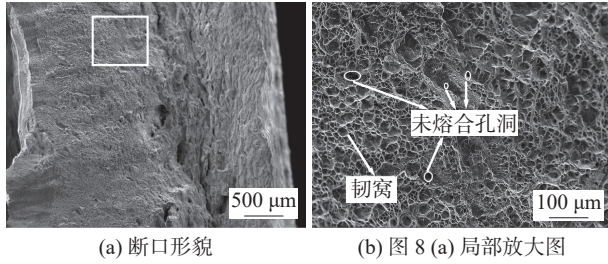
Inconel 600 镍基合金 PA + TIG 接头断口形貌
